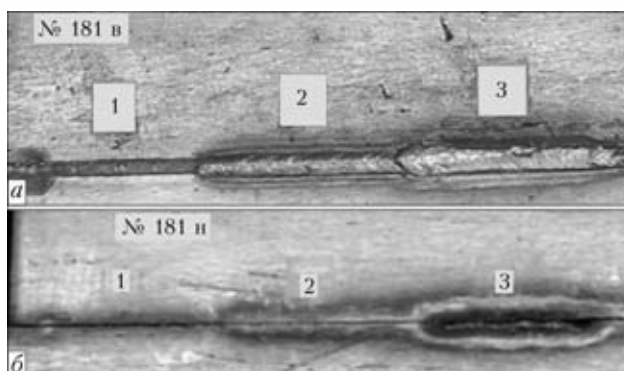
Образцы № 181 стыкового соединения из стали 08X17T ($\delta = 3,5$ мм): *a* — лицевая сторона; *б* — обратная сторона; 1 — лазерная сварка; 2 — плазменная сварка; 3 — гибридная сварка
